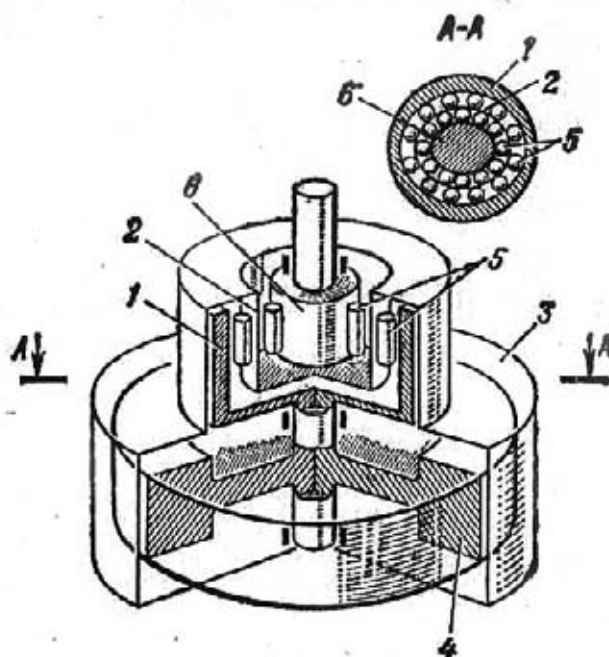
Передача вращения через герметичный корпус волновой муфтой
